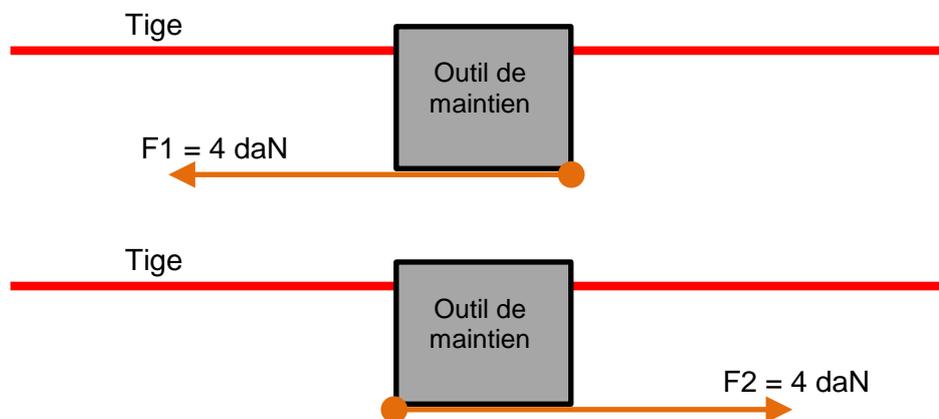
Dispositif d'essai de glissement pour outil de maintien
